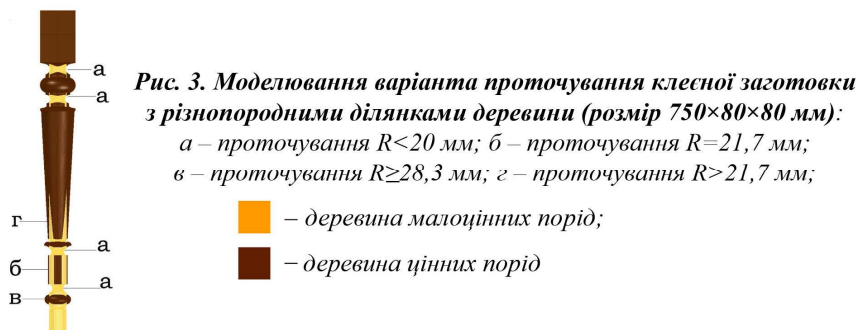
Моделювання варіанта проточування клеєної заготовки з різнопорідними ділянками деревини (розмір 750×80×80 мм):
